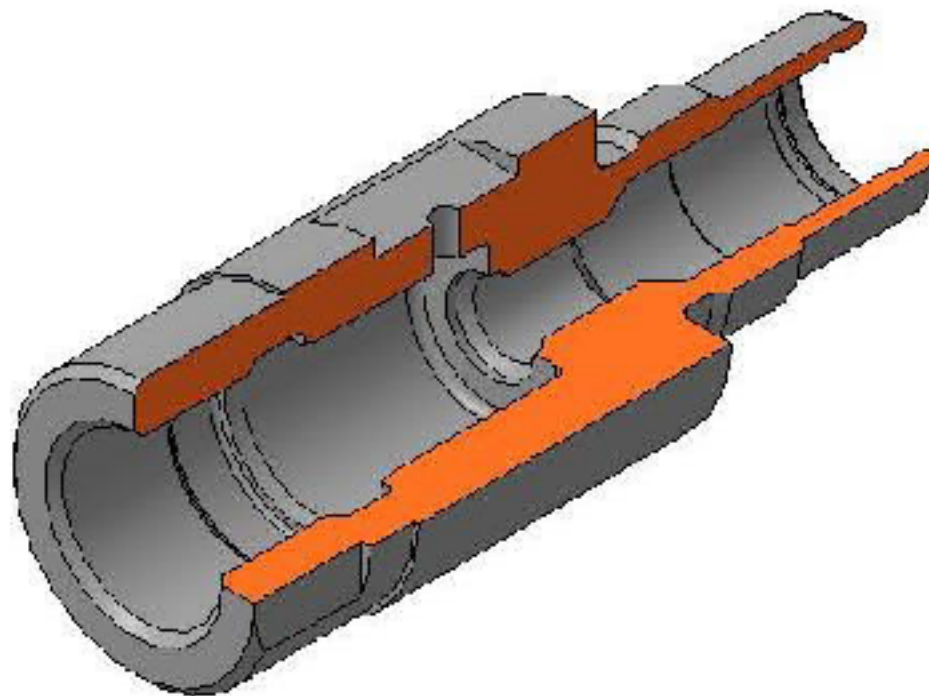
3D-модель деталі «Корпус клапана 12.01.004»
